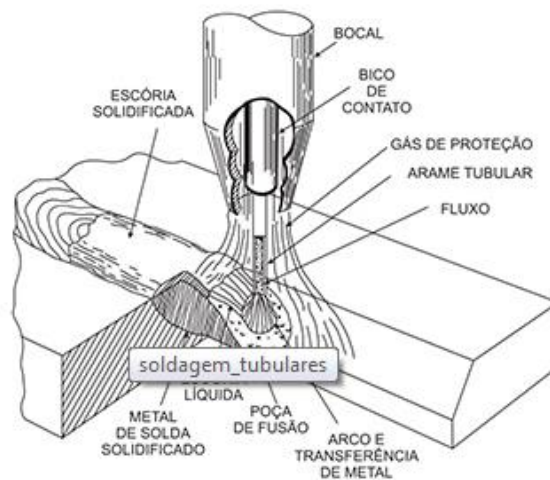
Soldagem com arame tubular - Fonte: Apostila ESAB
